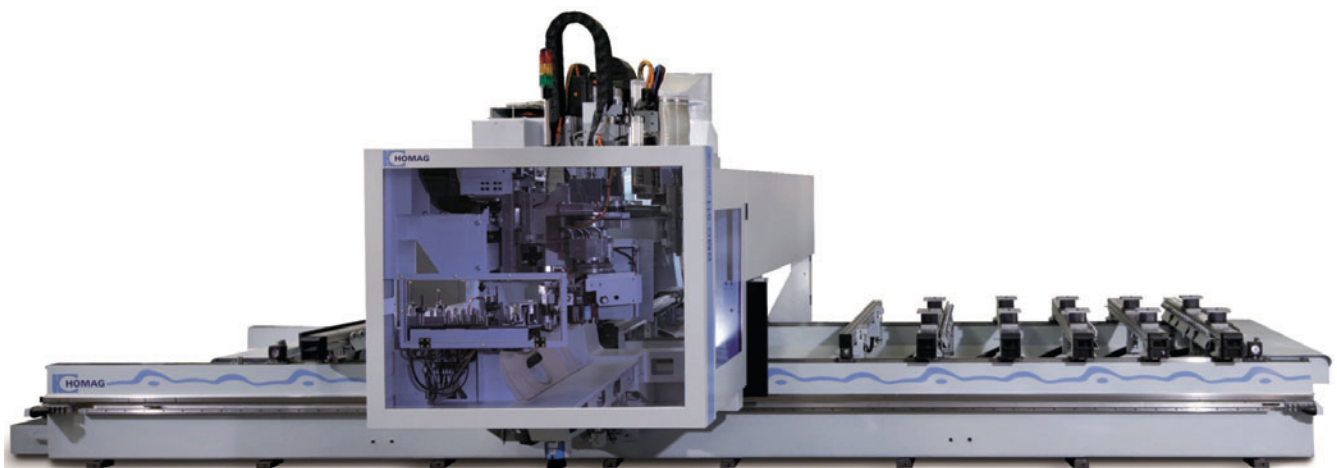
Machine d'usinage du bois sur un banc en BUHP
